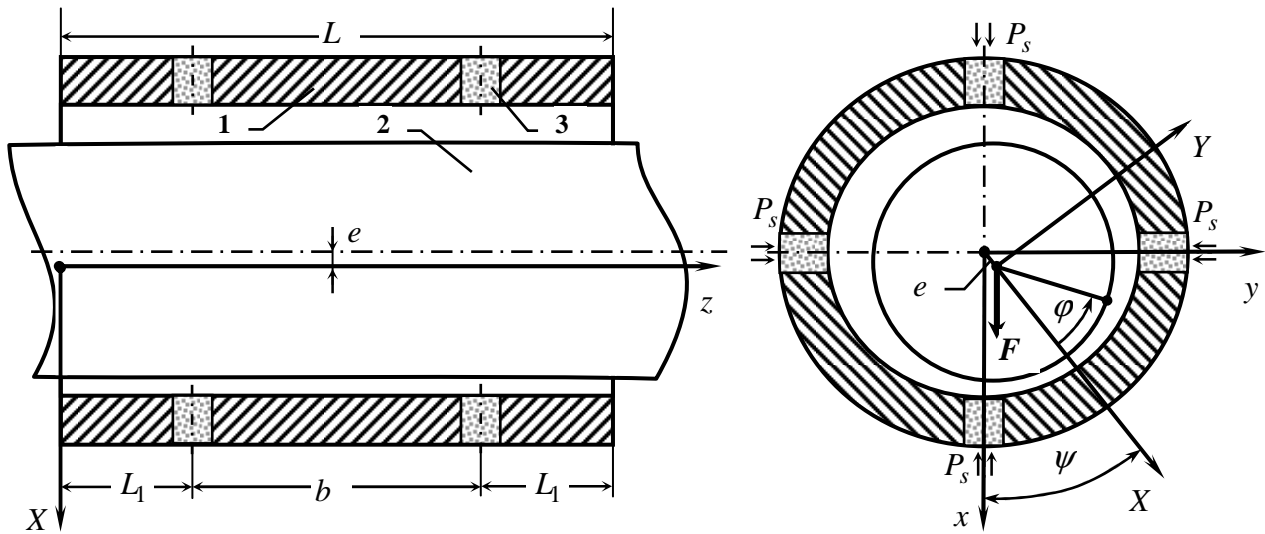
Газовый подшипник с двумя рядами пористых вставок:
